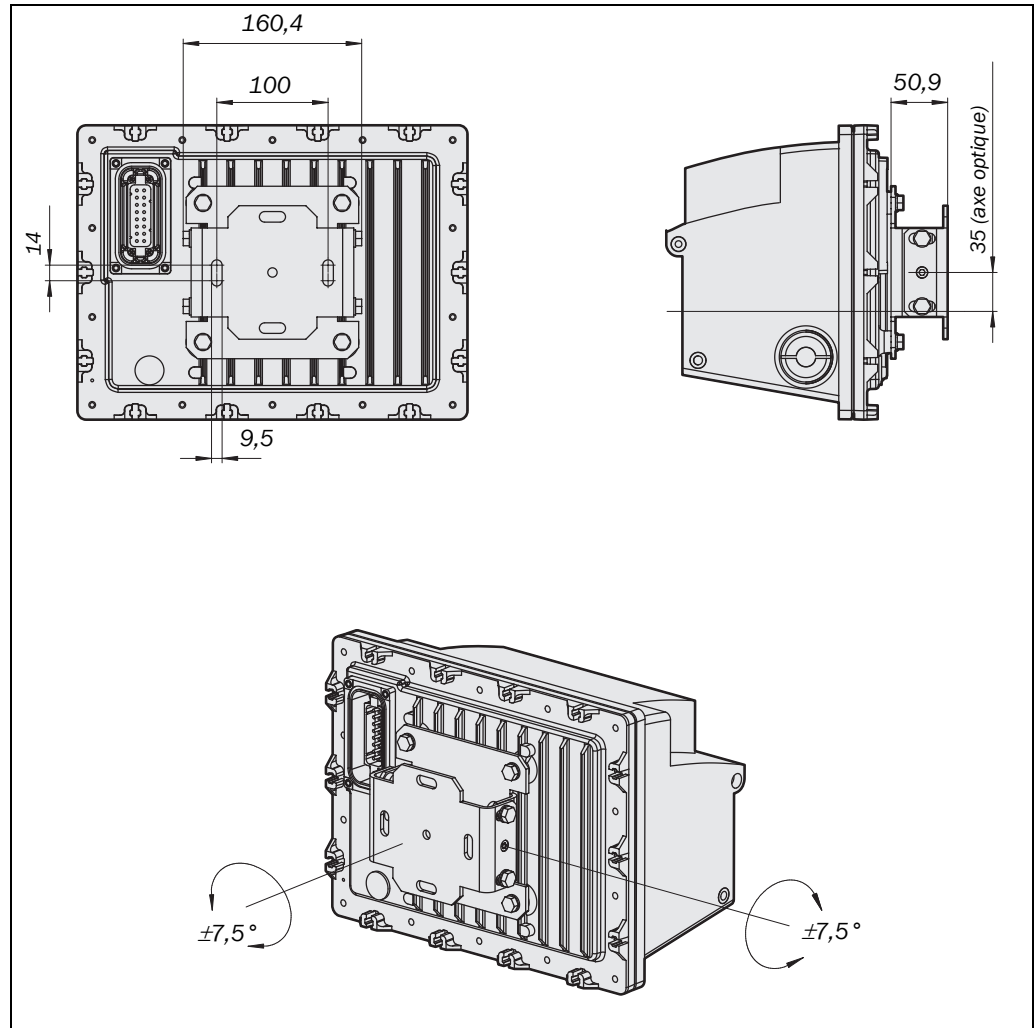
Schéma coté du support réglable pour S3000 Cold Store (mm)
